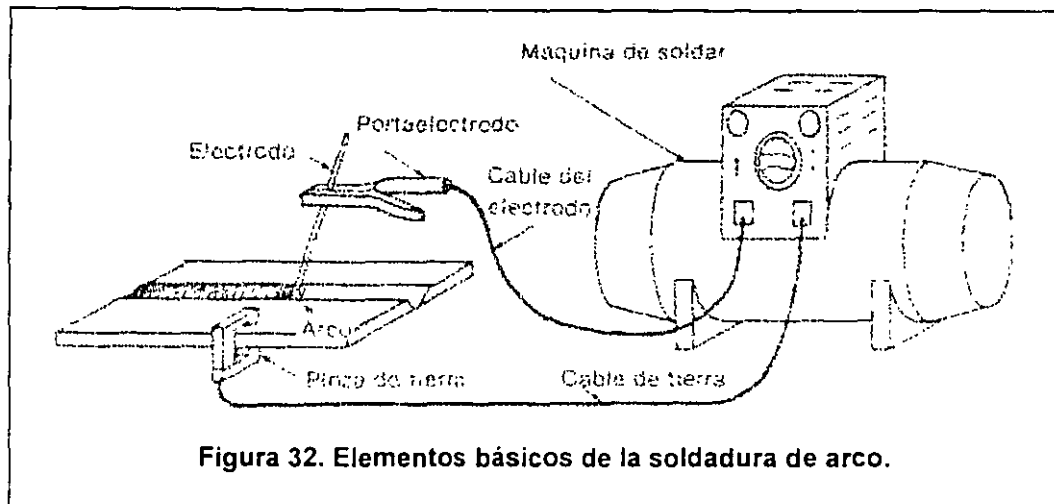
Elementos básicos de la soldadura de arco.
